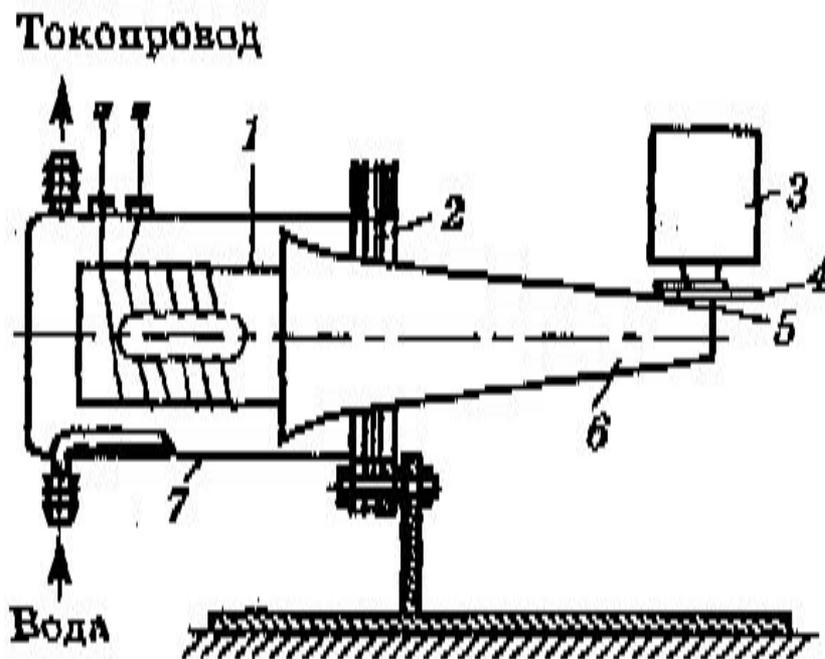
Схема установки для точечной сварки ультразвуком
